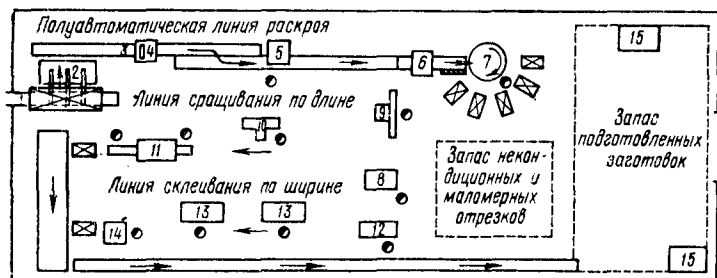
Схема планировки оборудования в раскройном цехе (поперечно-продольный раскрой):
